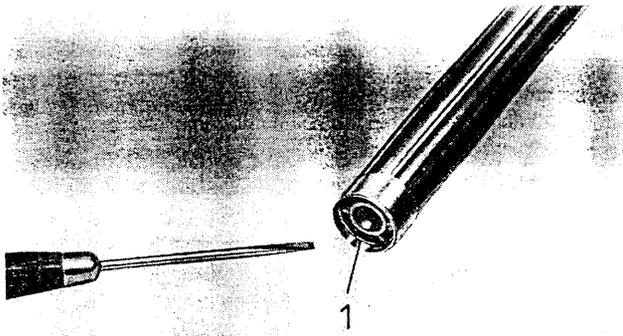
Faire sortir en pressant la bague ronde du tube de guidage
